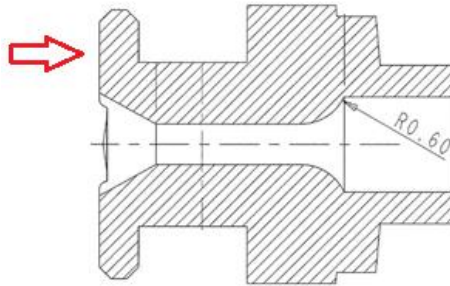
Posible punto de inyección, en la parte superior de la pieza
